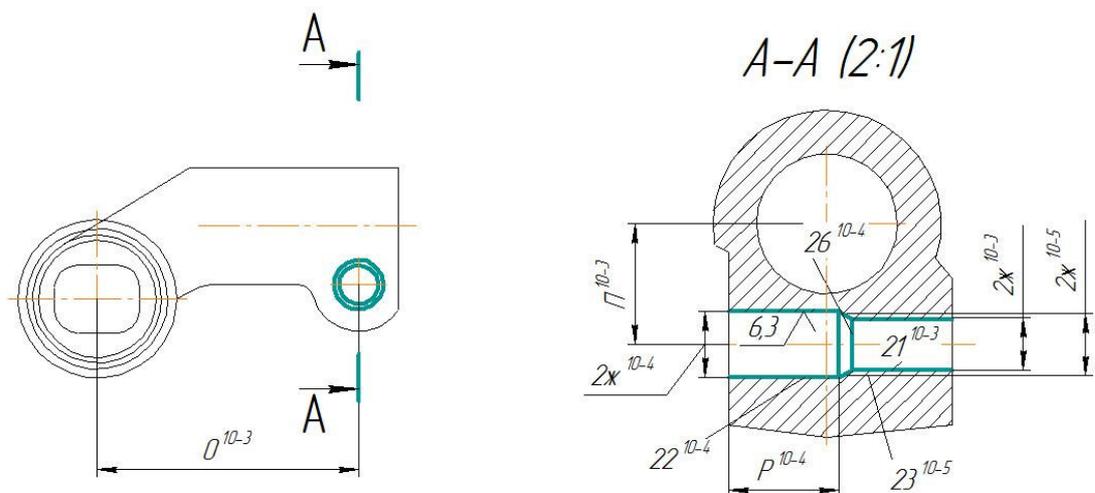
Сверление, рассверливание, нарезание резьбы
